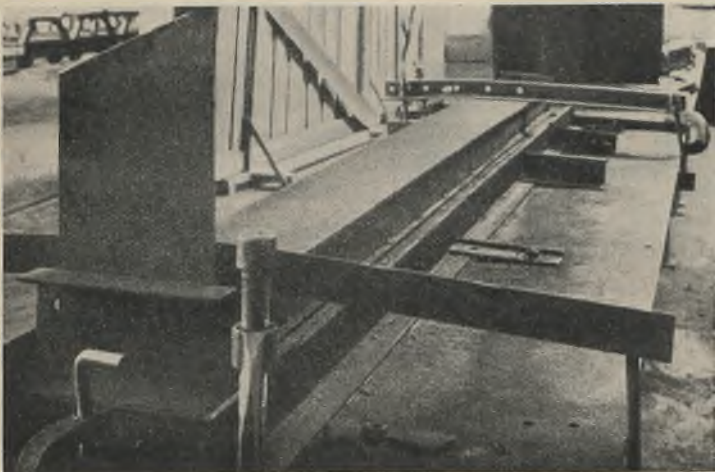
Stützenschaft im Kiesbett ruhend, fertig zum Schweißen.
